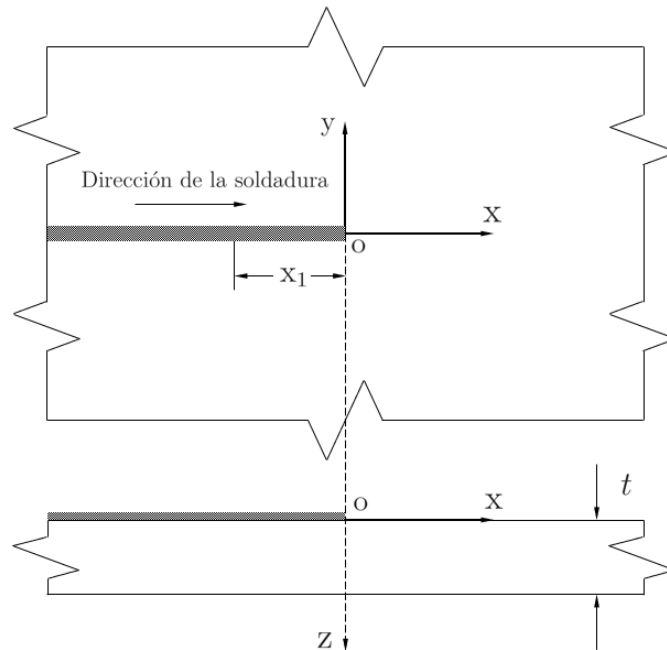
Soldadura tipo *bead-on-plate* en placa ancha. [7]
